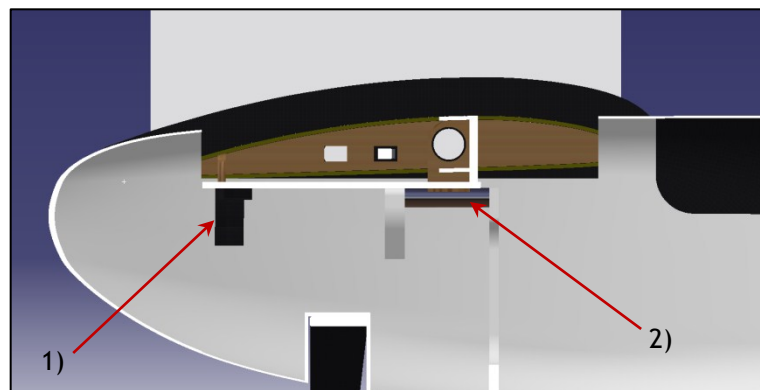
Vista em CAD do corte do plano longitudinal da asa telescópica e da plataforma UAV de testes com: 1) ponto de fixação em L, 2) tubo de alumínio.
